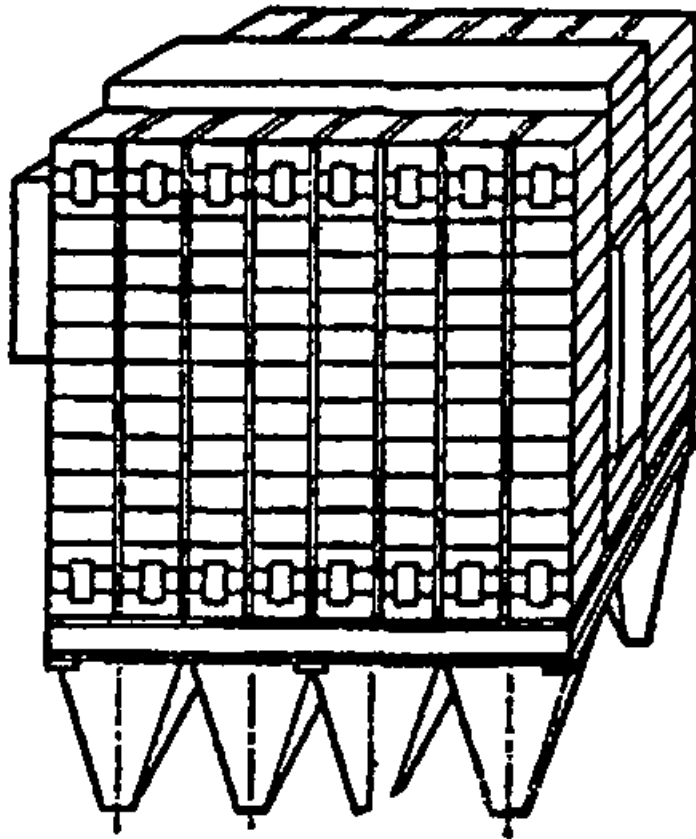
Схема корпусу рукавного 10-секційного фільтру ФРО-20000
